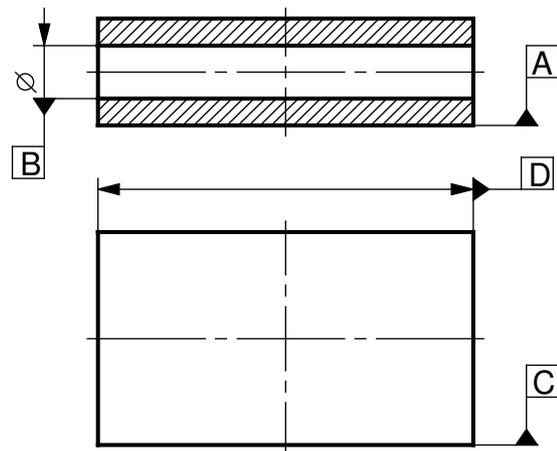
Bezeichnung der Bezugselemente für das Werkstück aus Bild 1
